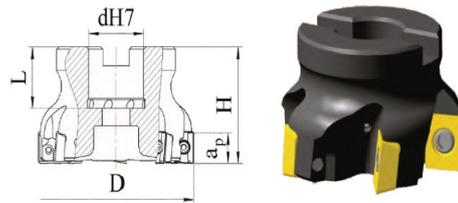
Торцовая насадная фреза с расположением главной режущей кромки параллельно оси вращения фрезы ( $\varphi = 90^\circ$ )
